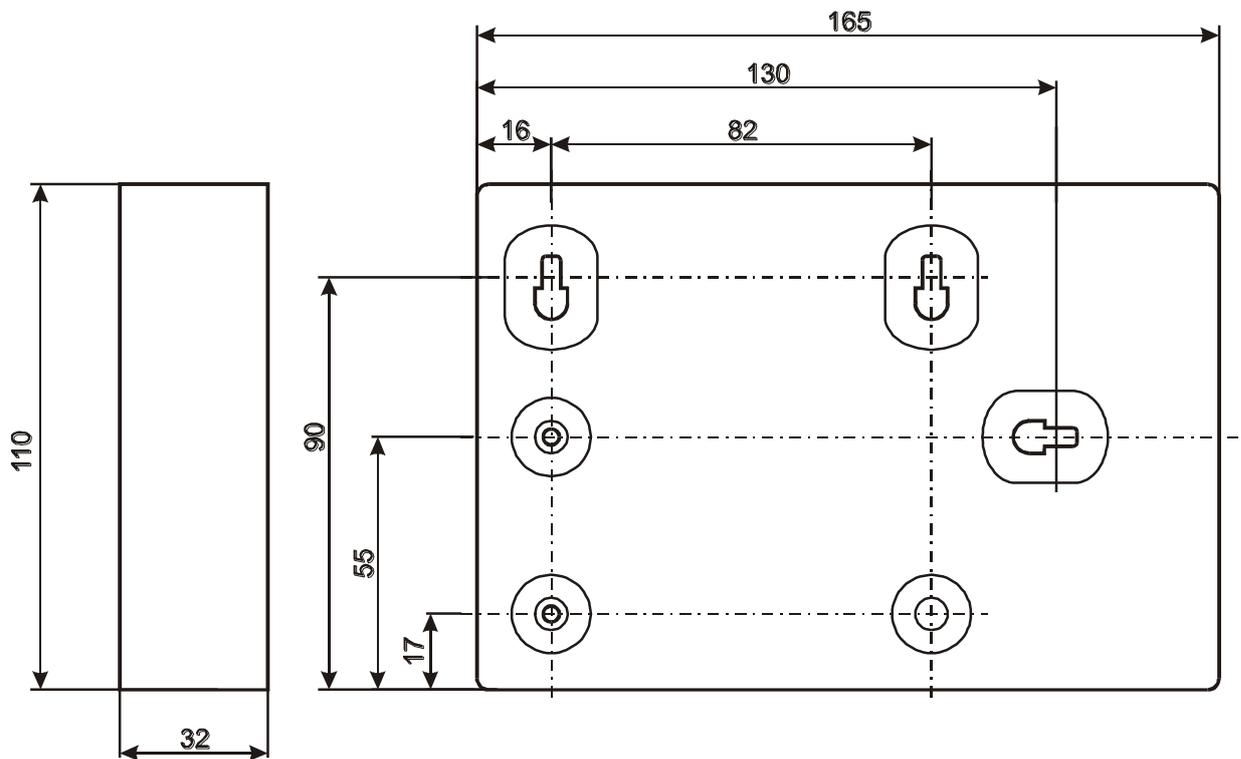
Внешний вид, габаритные и присоединительные размеры (исполнение IP20)
